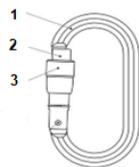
1 - скоба; 2 - защелка; 3 - резьбовая муфта
